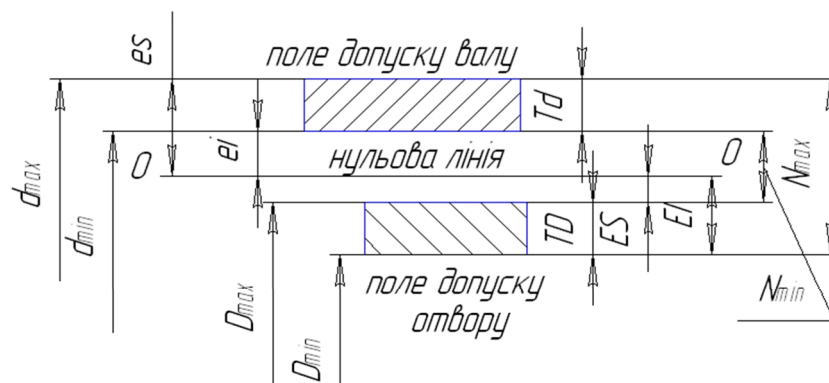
Схема полів допусків вала і отвору для посадок з натягом
